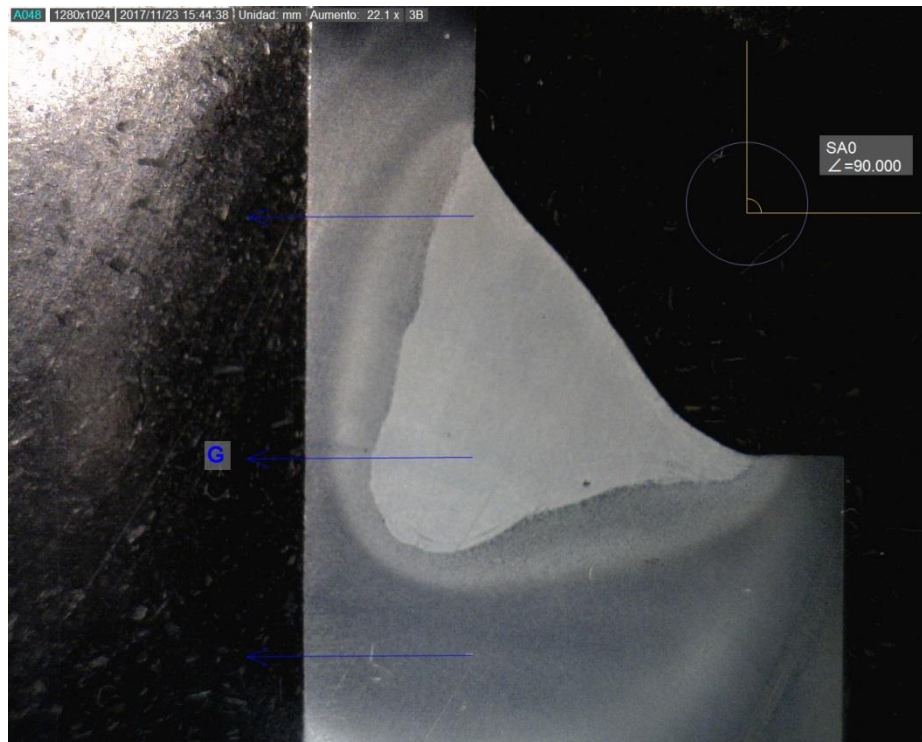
7 Perfil obtenido en cupón de soldadura 4A.
